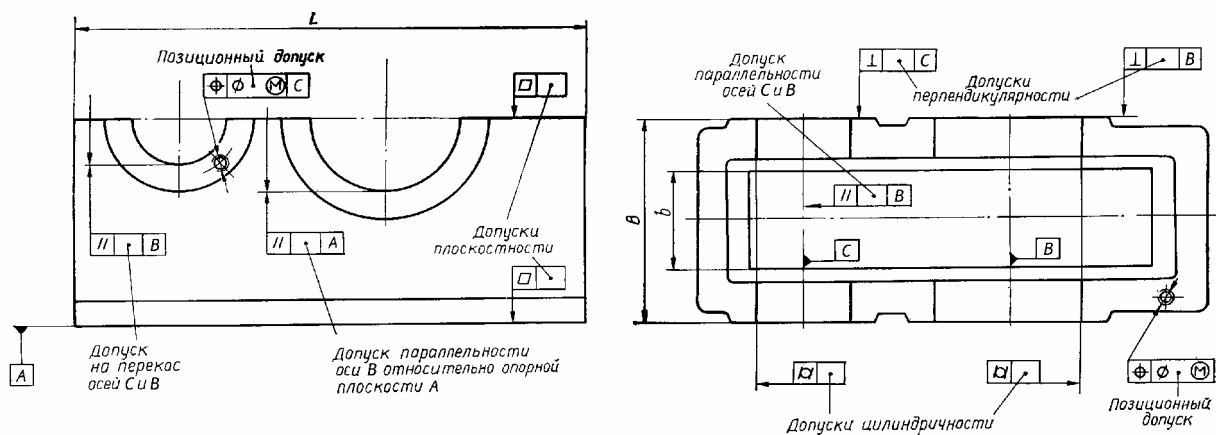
Допуски формы и расположения элементов корпусных деталей
